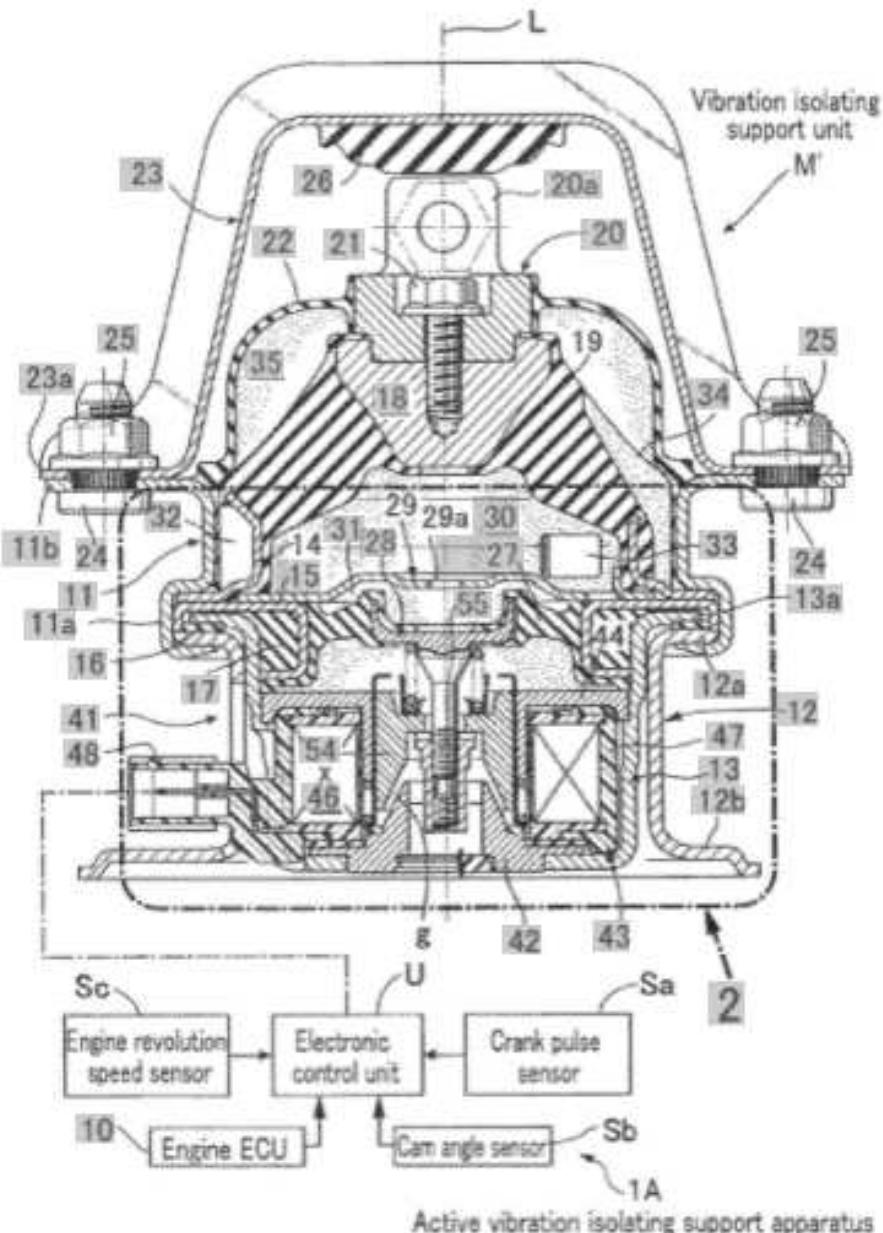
Установка активного виброизолирующего опорного устройства в двигатель транспортного средства
